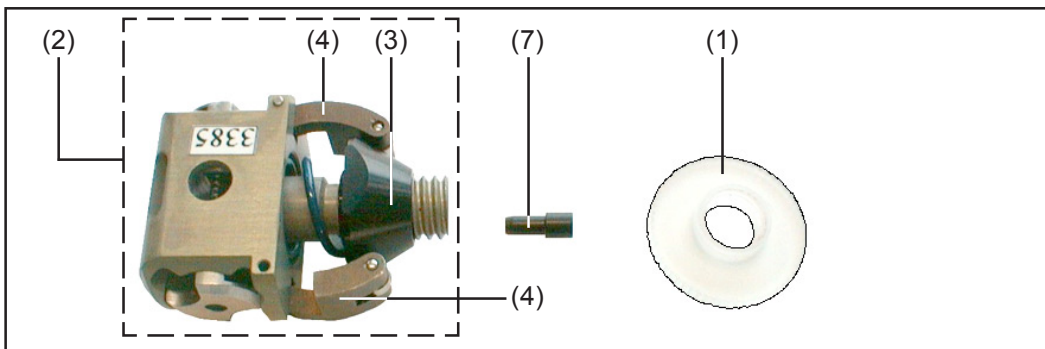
Dévisser l'écrou moleté et retirer la bague conique
